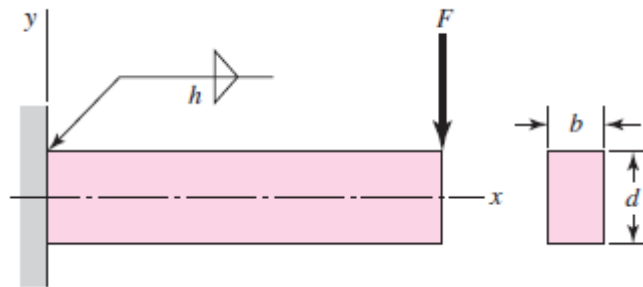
Voladizo soldado sujeta a flexión.
